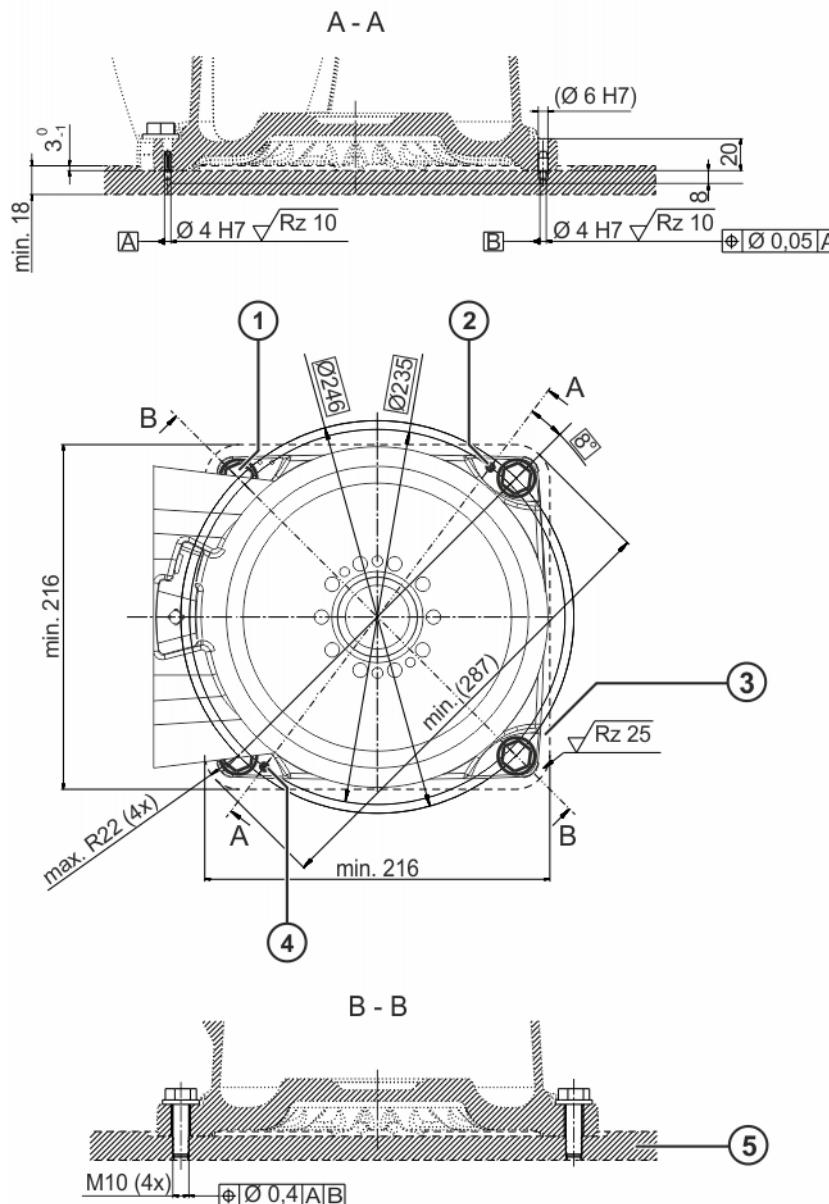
Maschinengestellbefestigung, Maßzeichnung
